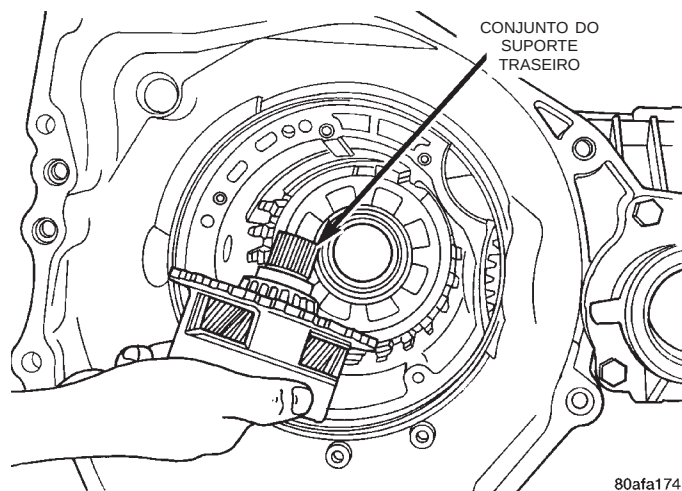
Remoção do Conjunto do Suporte Traseiro
